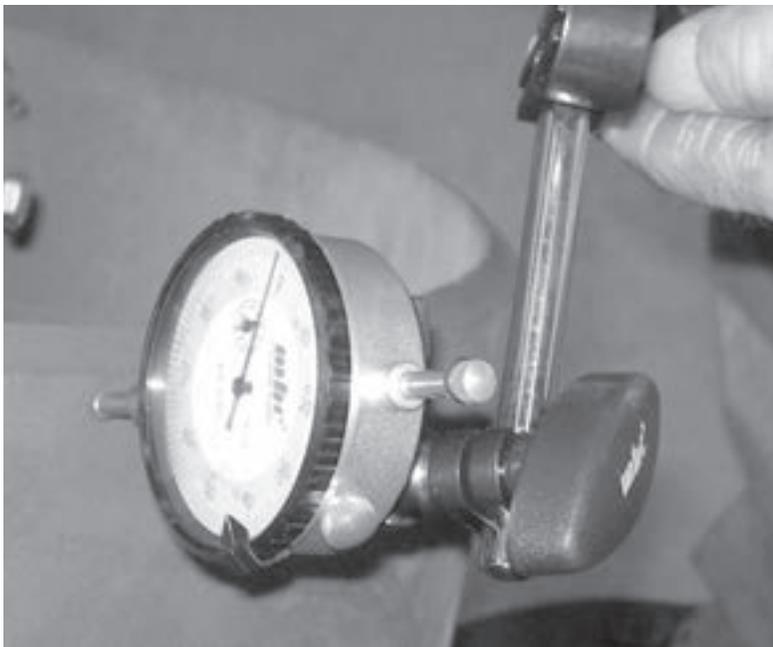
Coloque la punta del indicador de modo que toque el tubo, perpendicular a la superficie.
